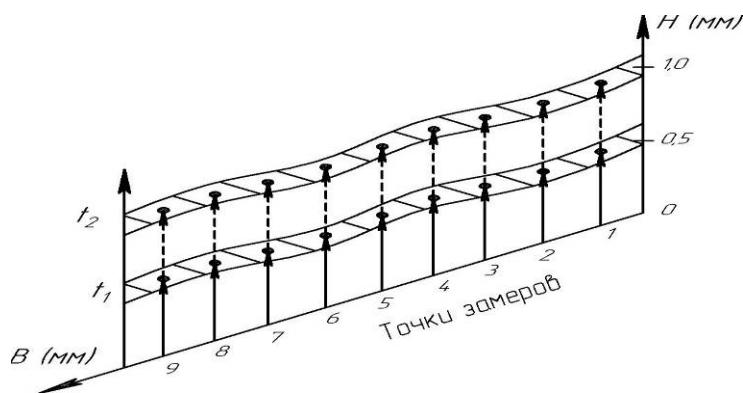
Степень износа контрольных точек режущей кромки детали планка ( $t_1$ - контрольный рубеж 240 часов;  $t_2$ - контрольный рубеж 360 часов)
